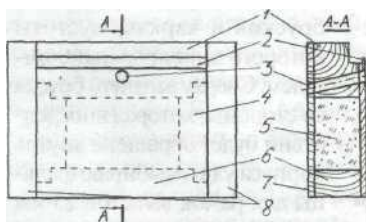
Передняя стенка корпуса в сборе (240x375 мм): 1 — верхний брусок; 2 — металлическая пластинка; 3 — верхний леток; 4 — боковой брусок; 5 — наполнитель; 6 — нижний брусок; 7 — фанера; 8 — выступающая часть фанеры с лицевой стороны передней и задней стенок
